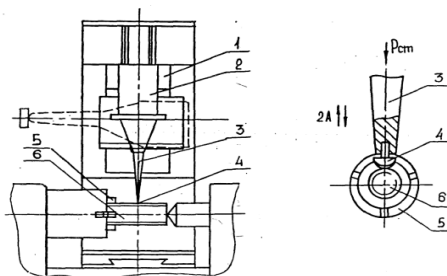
Устройство для обработки металлических поверхностей шариками
